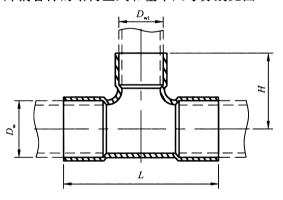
异径三通 RT 承插式钎焊铜管件
